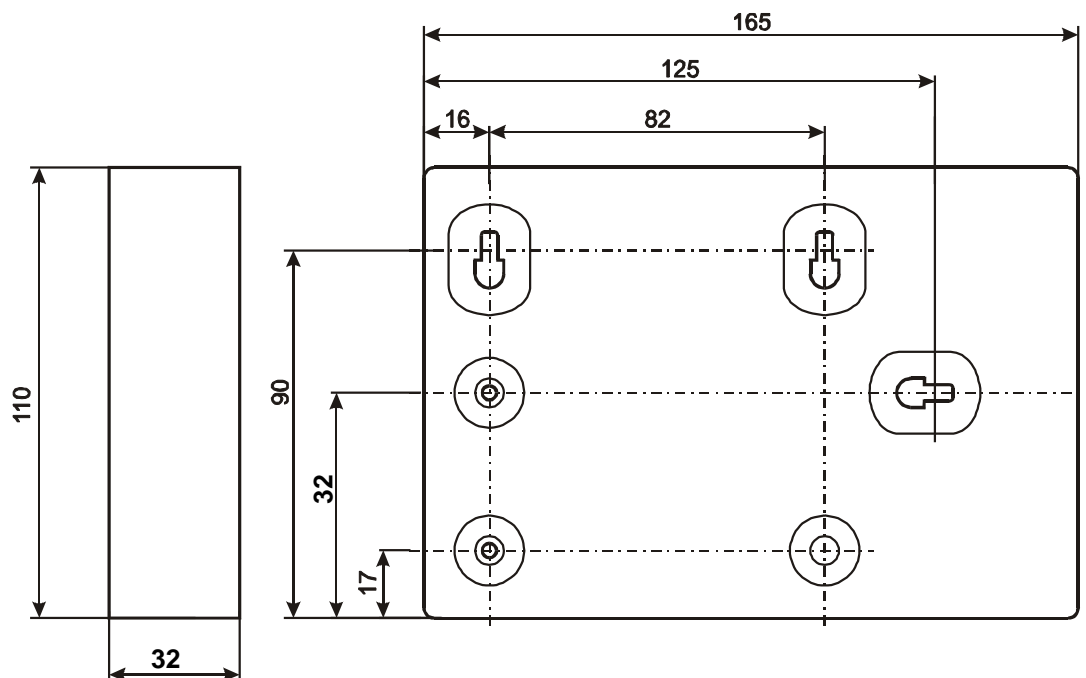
Внешний вид и габаритные размеры СК-01 в исп. IP20
